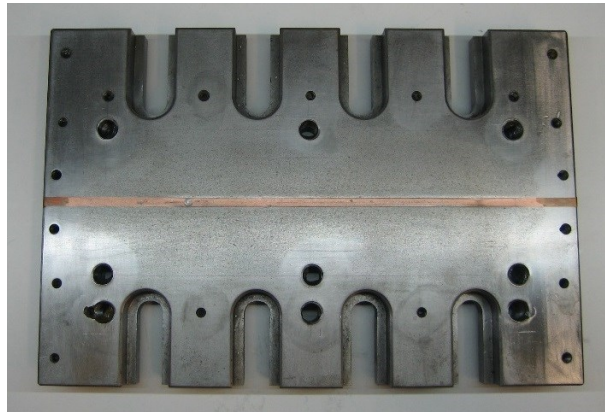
Base de soldadura condutora, em aço, com cobre no eixo de simetria. Dimensões: 300×200×35 mm.
